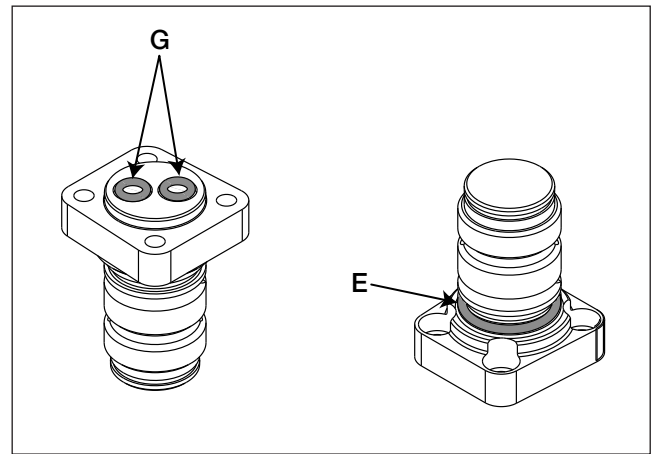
Anbringung des O-Rings, Schwenkkupplungsstange
